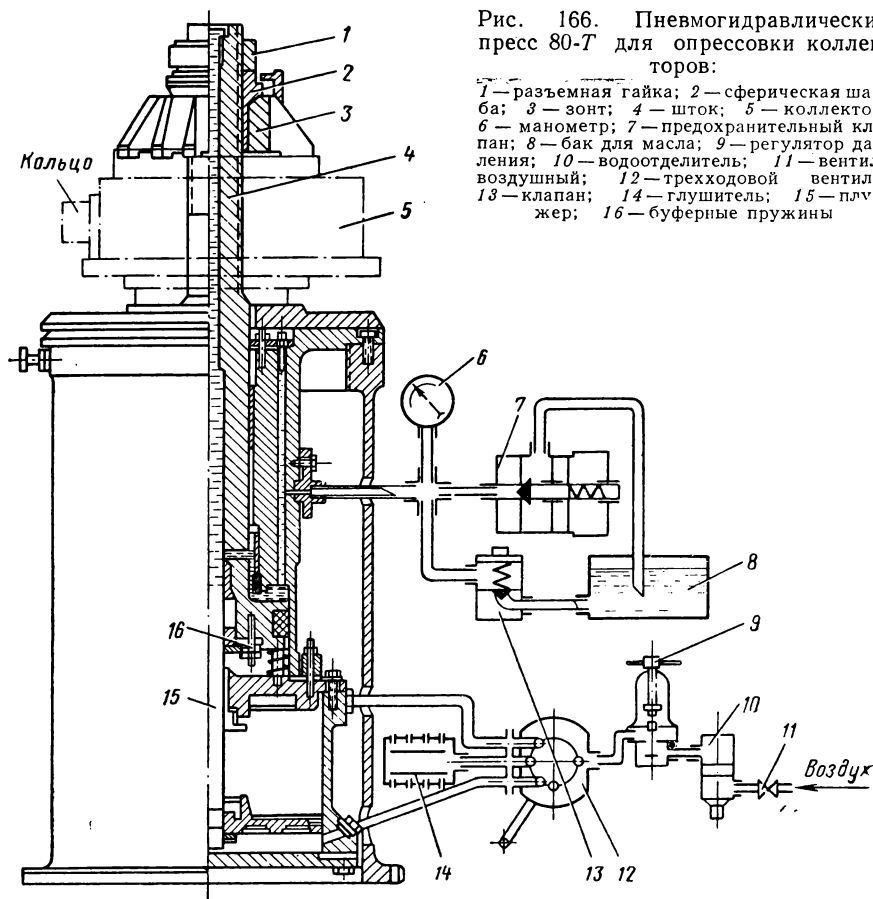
Пневмогидравлический пресс 80-Т для опрессовки коллекторов:
